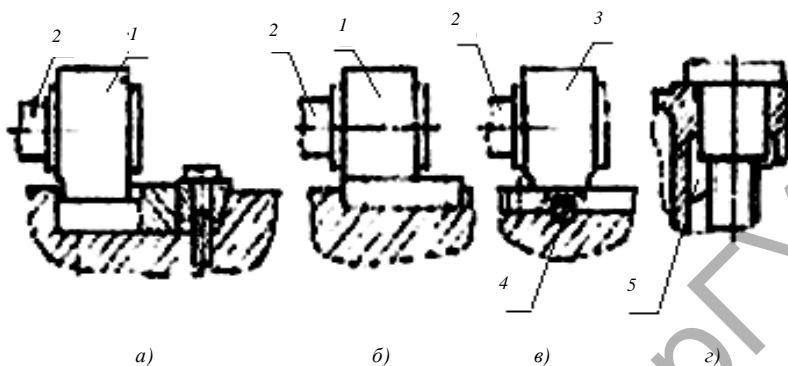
Схемы закрепления корпуса опоры винта привода подачи
